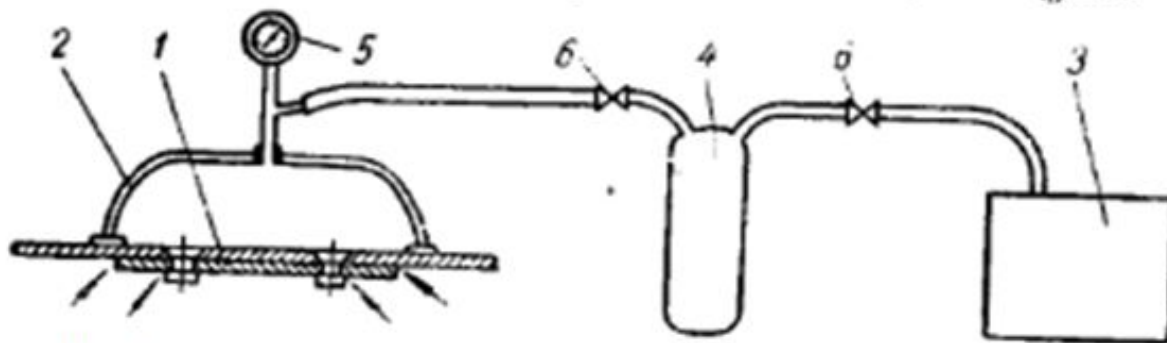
Схема установки для контроля герметичности заклепочного шва:
